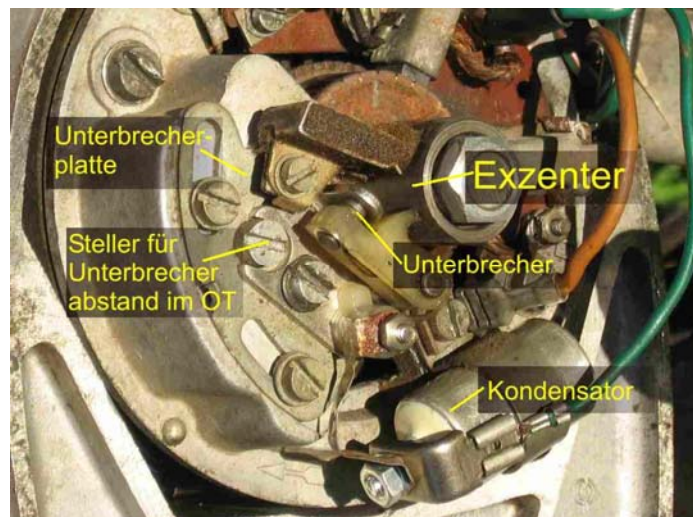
Ansicht der wichtigsten Teile der mechanischen ES/TS Zündanlage
